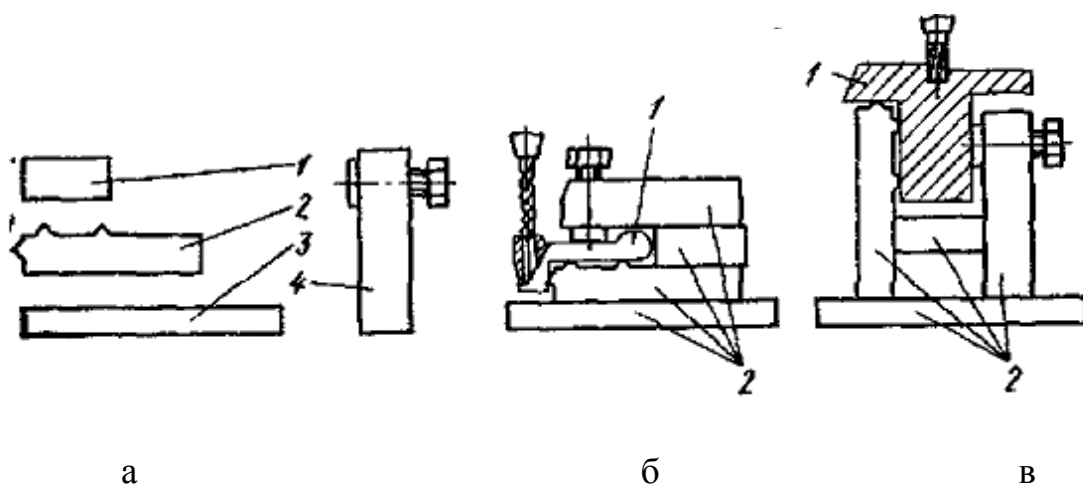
Группа нормализованных деталей и узлов (а), используемых для компоновки приспособлений: для сверления отверстий в рычаге (б); для фрезерования паза в корпусе (в).
